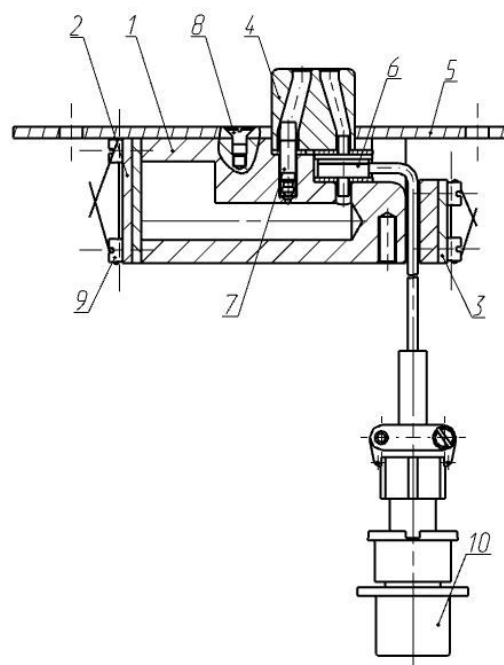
Конструктивная схема модуля измерения пульсаций давления: 1 – корпус; 2,3 – фланец; 4 – корпус двухканальный; 5 – планка; 6 – датчик давления ДМИ-0,6-II; 7 – демпфер Д59-II; 8,9 – винт; 10 – штексельный разъём
